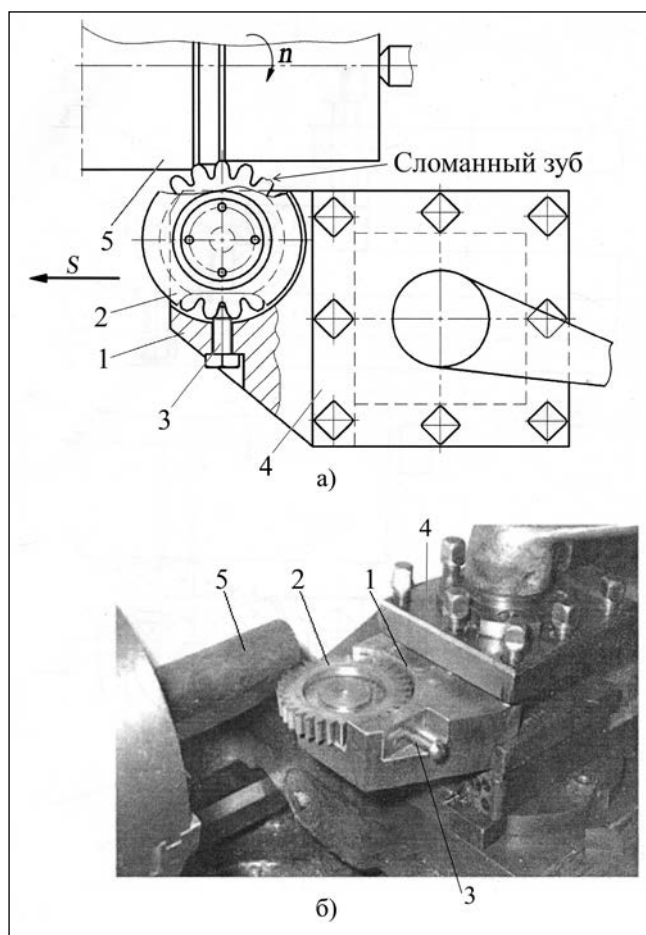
Точение долбяком: а) приспособление в резцедержателе токарного станка, б) рабочая зона
